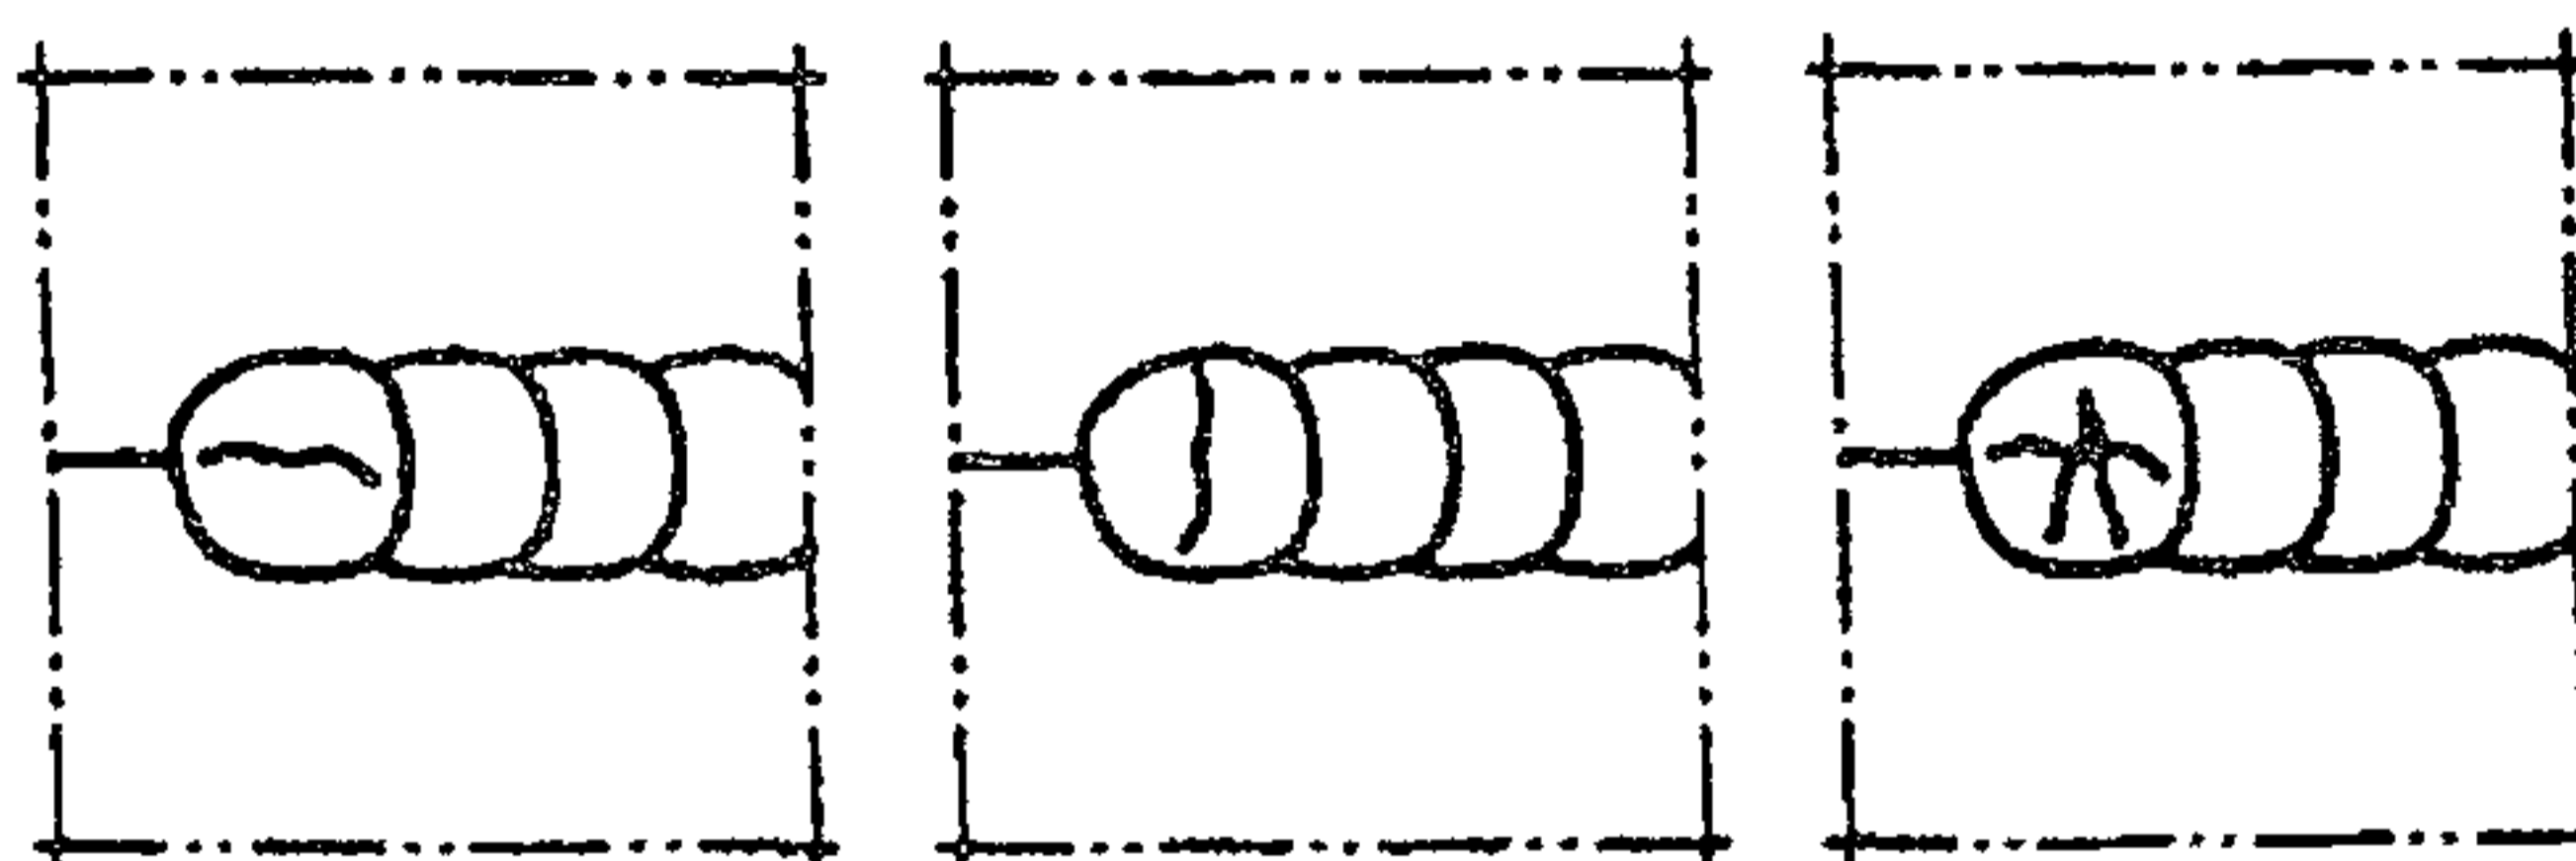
Кратерные трещины сварного соединения
